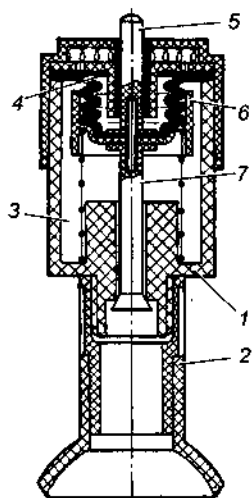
Индикатор засоренности воздушного фильтра: 1 — диск; 2 — красный барабан; 3 — камера; 4 — прокладка; 5 — колпачок; 6 — поршень; 7 — клапан
